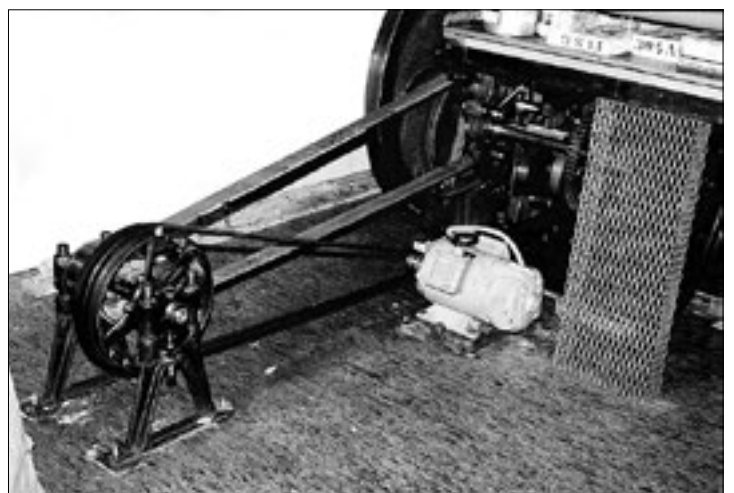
En 3 hkr släpringad elmotor på 1 400 varv/min driver tryckpressen över en remväxel.
